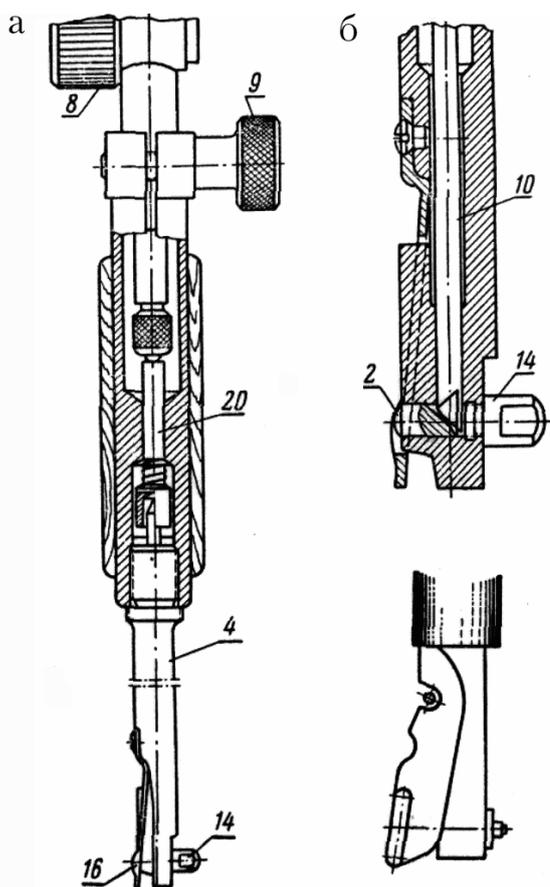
Индикаторный нутромер с клиновой передачей:
